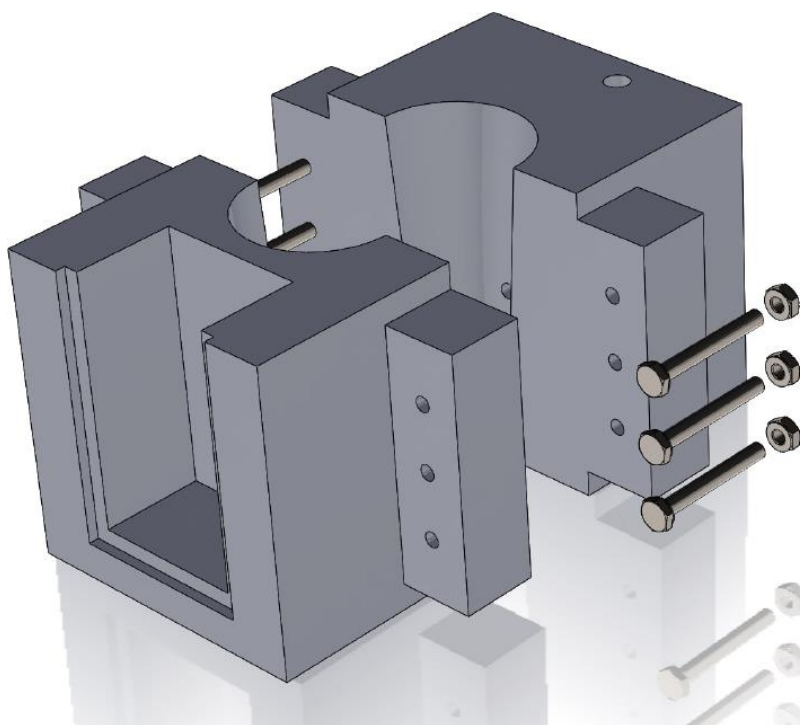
Esquema do projeto do suporte e da montagem suporte e fresa.
